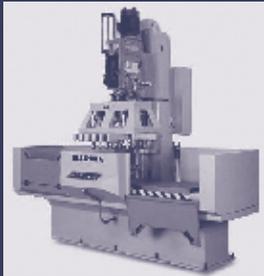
Posicionadores de piezas (Fuente: Bugo Systems).
